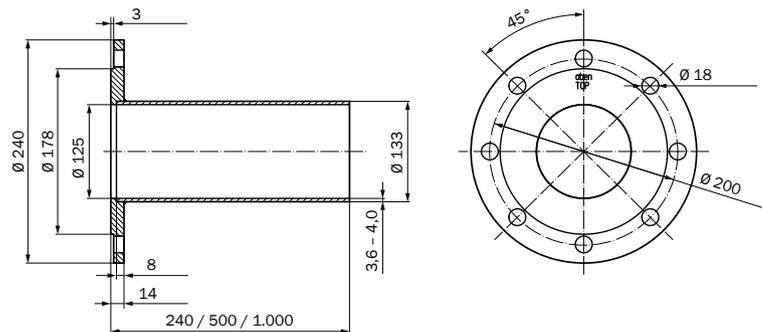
Bride de montage DN100 (toutes cotes en mm)
